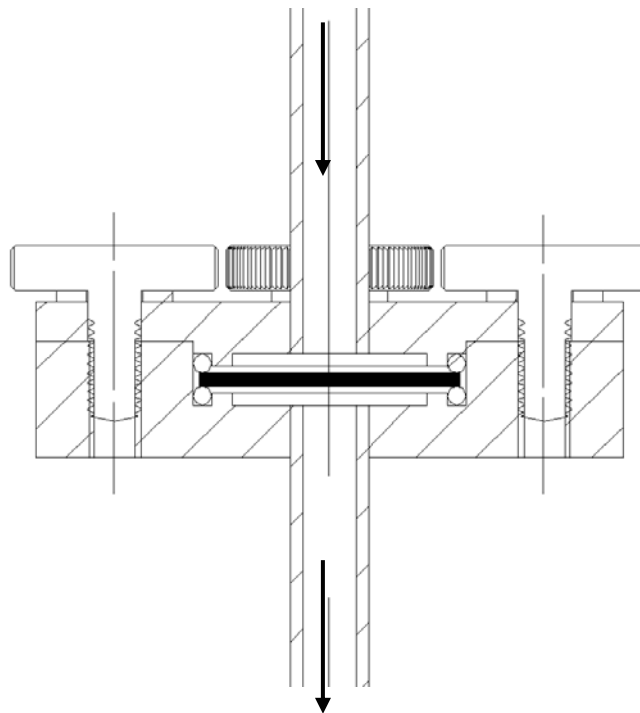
Meßzelle des Lecksuchers: Im Inneren liegt die durch zwei O-Ringe zu den Seiten abgedichtete, beschichtete Keramik (schwarz). Der obere Teil der Meßzelle wird mit vier Schrauben auf dem unteren Teil befestigt. Die Pfeile geben die Richtung des Gasflusses an.
